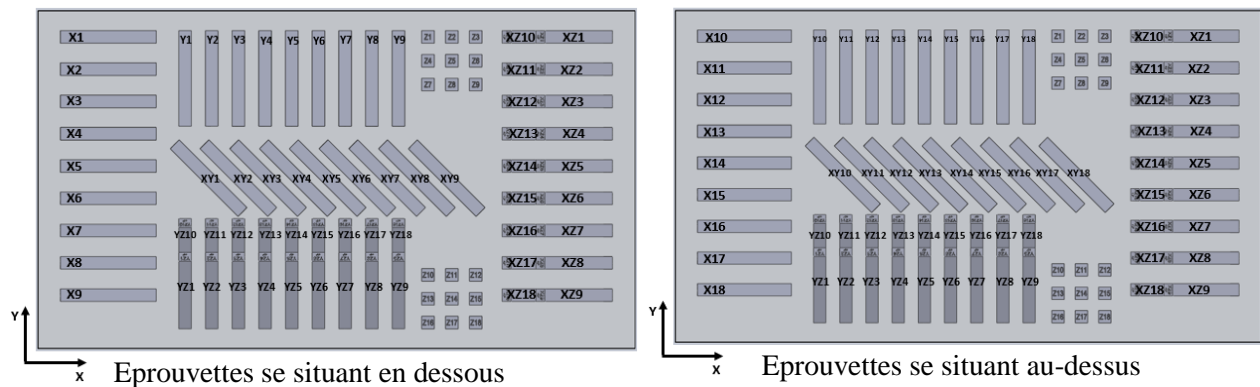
Vue 2D du premier et second niveau d'éprouvettes.
